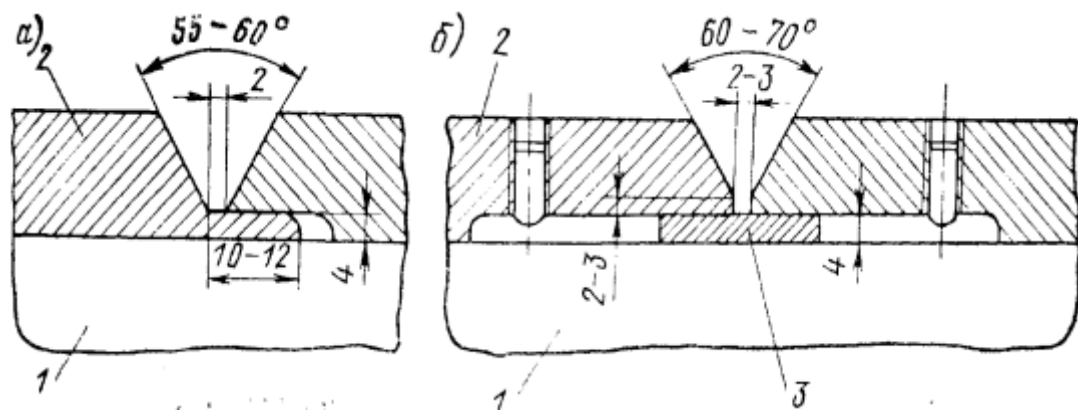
Підготовка під зварювання з'єднання складових облицювань:
